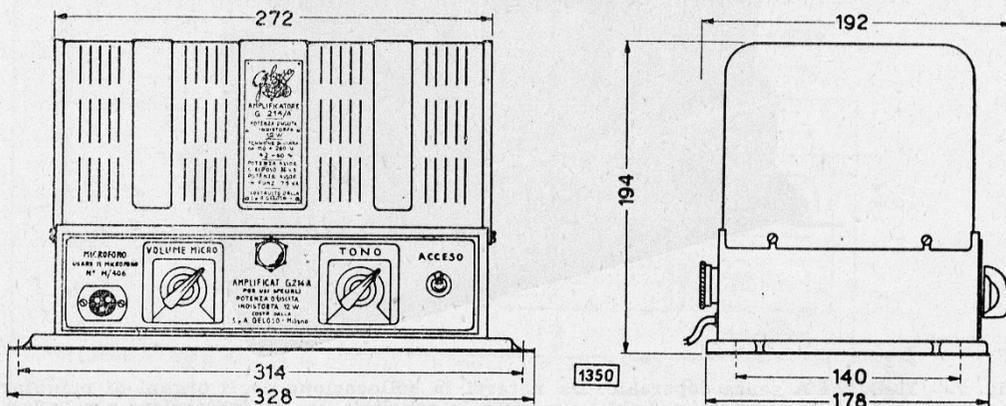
Le dimensioni di ingombro del G. 214/A.
